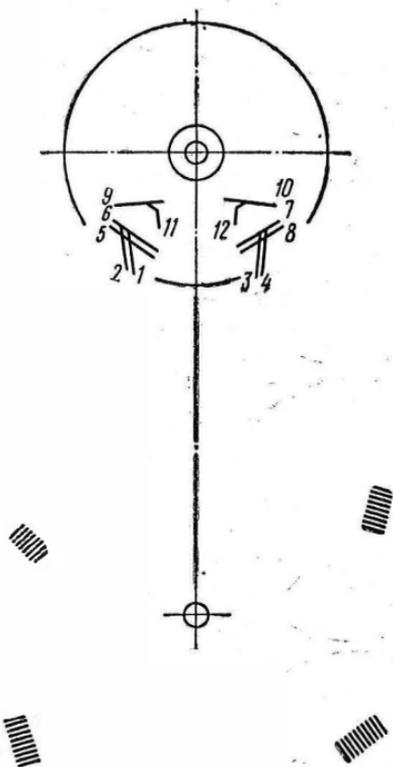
Проекторный чертеж для отладки хода с базированием по пазу анкерной вилки и рожкам
